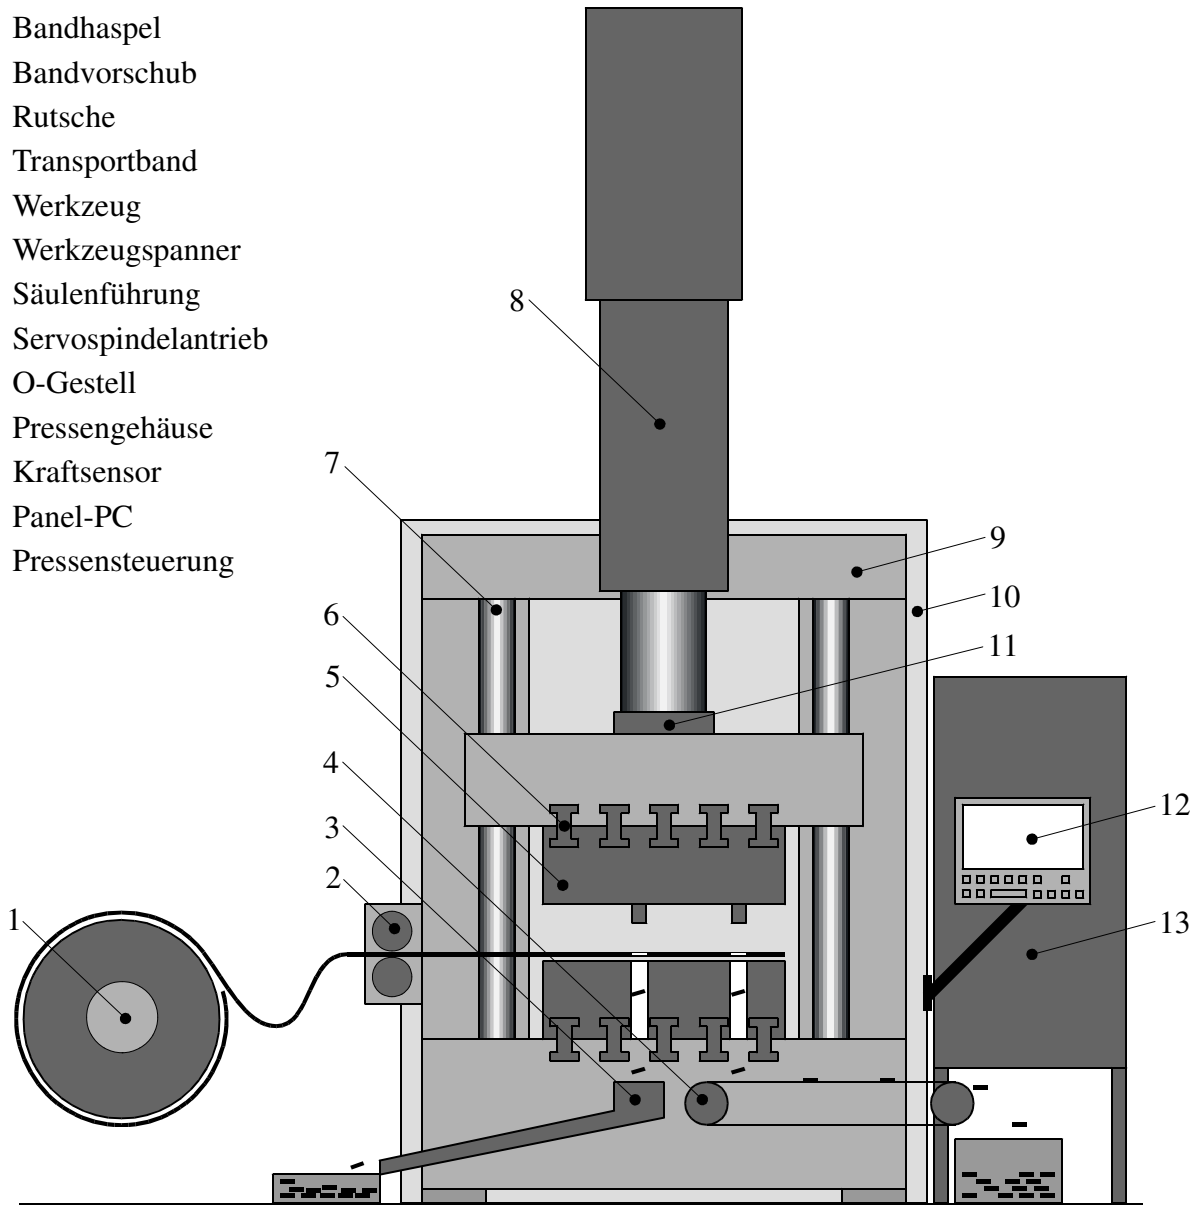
Aufbau einer Servospindelpresse zur Blechbearbeitung
